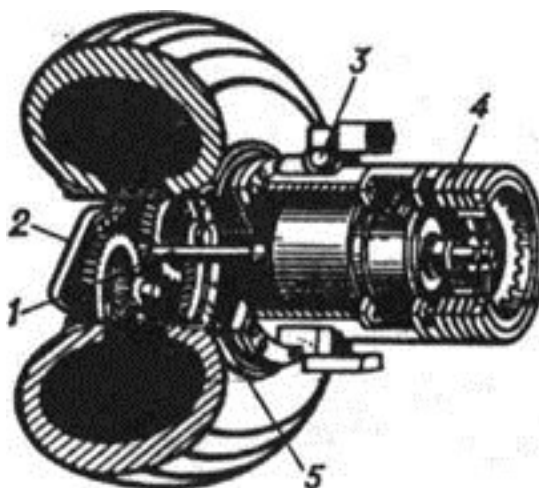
Мотор-колесо: 1 - вал электродвигателя; 2 - редуктор; 3 - цапфа; 4 - дисковый тормоз; 5 - зубчатый венец колеса
